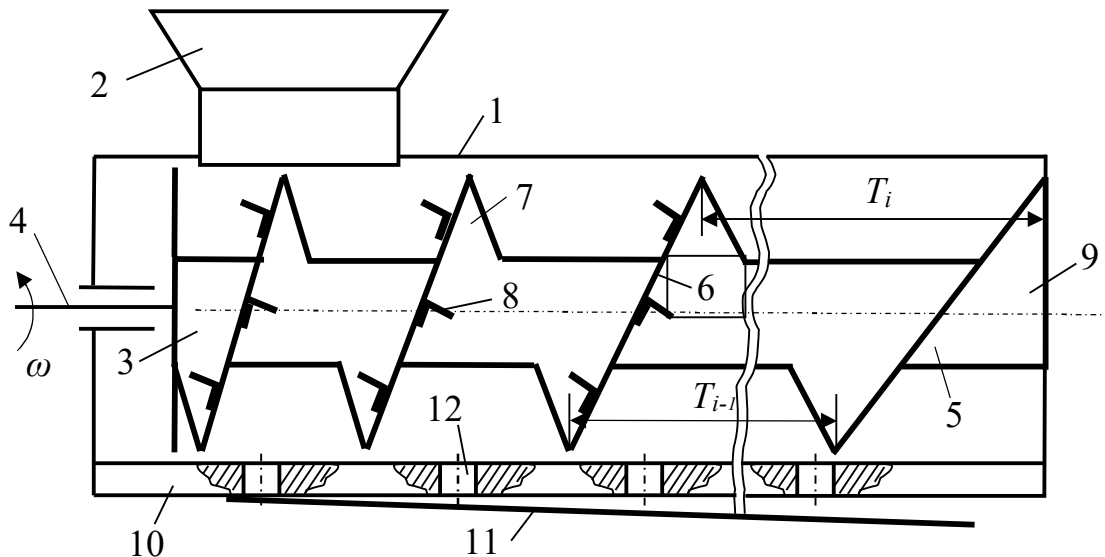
Конструктивно-компонувальна схема шнекового транспортера-подрібнювача з комбінованим робочим органом: 1 – кожух; 2 – бункер; 3 – шнек; 4 – приводний вал; 5 – барабан; 6 – гвинтова лінія; 7 – спіральний виток; 8 – Г-подібний ніж-подрібнювач; 9 – вивантажувальна частина; 10 – нижня частина; 11 – направляючий лоток; 12 – отвори
